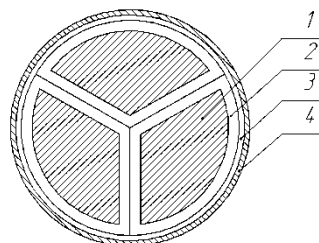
Модель кабеля. 1 – токопроводящая жила; 2 – фазная изоляция; 3 – поясная изоляция; 4 – металлический экран
